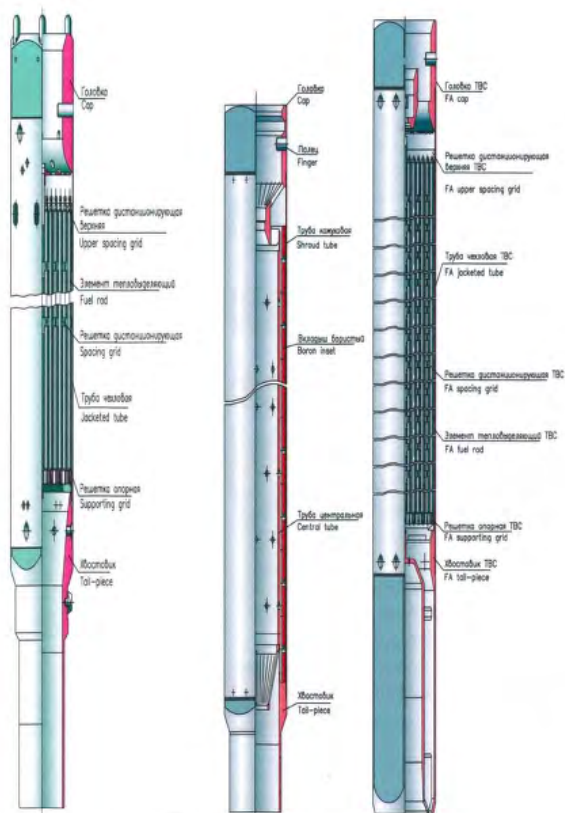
Чертежи общего вида базовой конструкции и топливных сборок РК и АРК (масштаб не соблюден)
